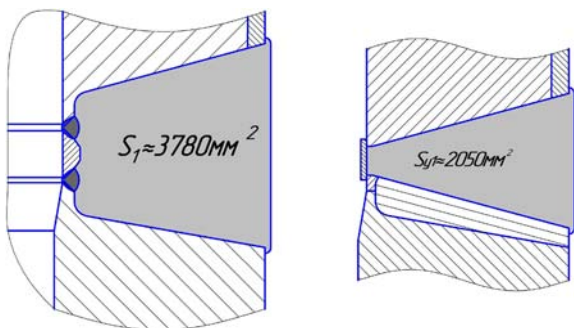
Площадь сечения сварного шва в зависимости от варианта подготовки кромок сварного соединения для автоматической сварки
